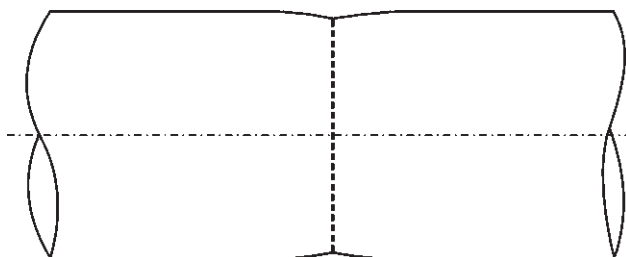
Несовершенство геометрической формы в зоне стыкового соединения, вызванное сваркой кольцевого шва
